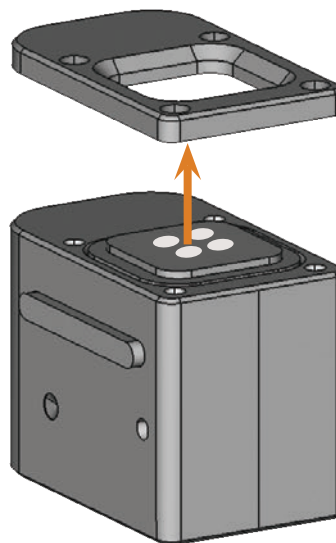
LEVANTAMIENTO DE LA CUBIERTA
